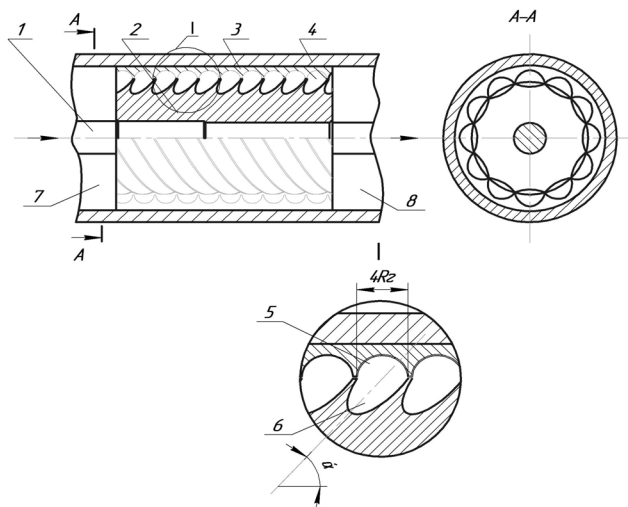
Удосконалені робочі органи ЛГН із статті [14]: 1 – привідний вал; 2 – гвинт; 3 – втулка; 4 – корпус; 5 – гвинтова канавка напівкруглої форми; 6 – гвинтова канавка довгастої форми; 7 – камера підводу; 8 – камера відводу.
